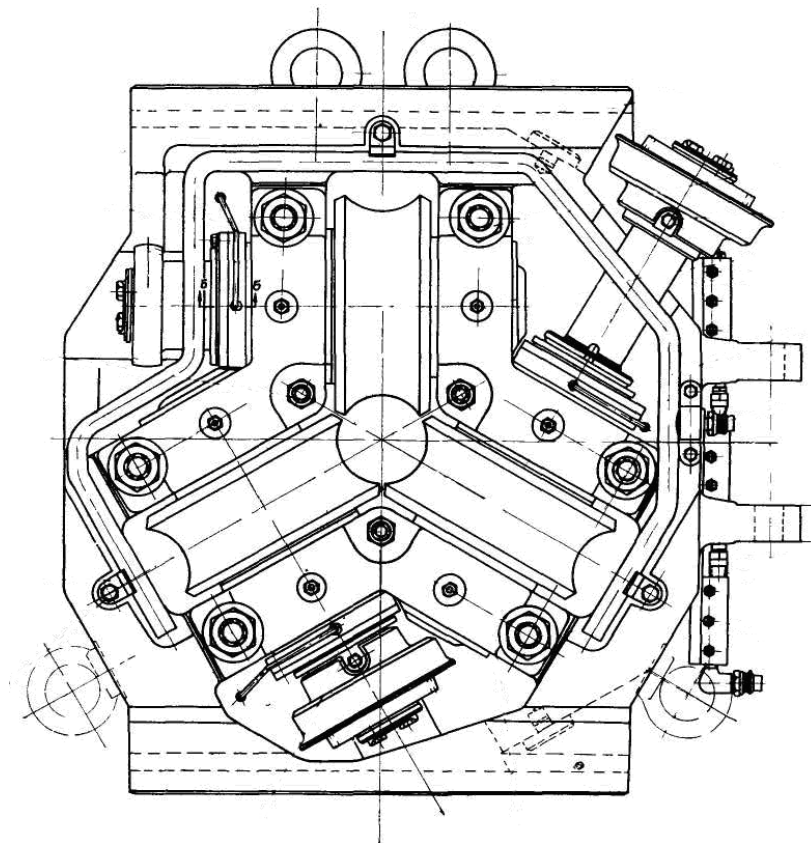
Рабочая клетка с раздельными приводами трех валков.
